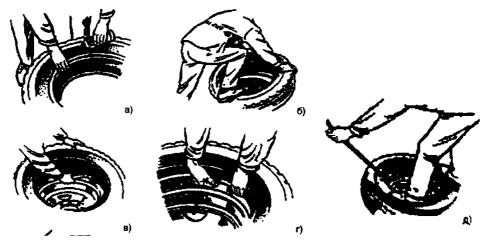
Ручной монтаж бескамерной шины на колесо
